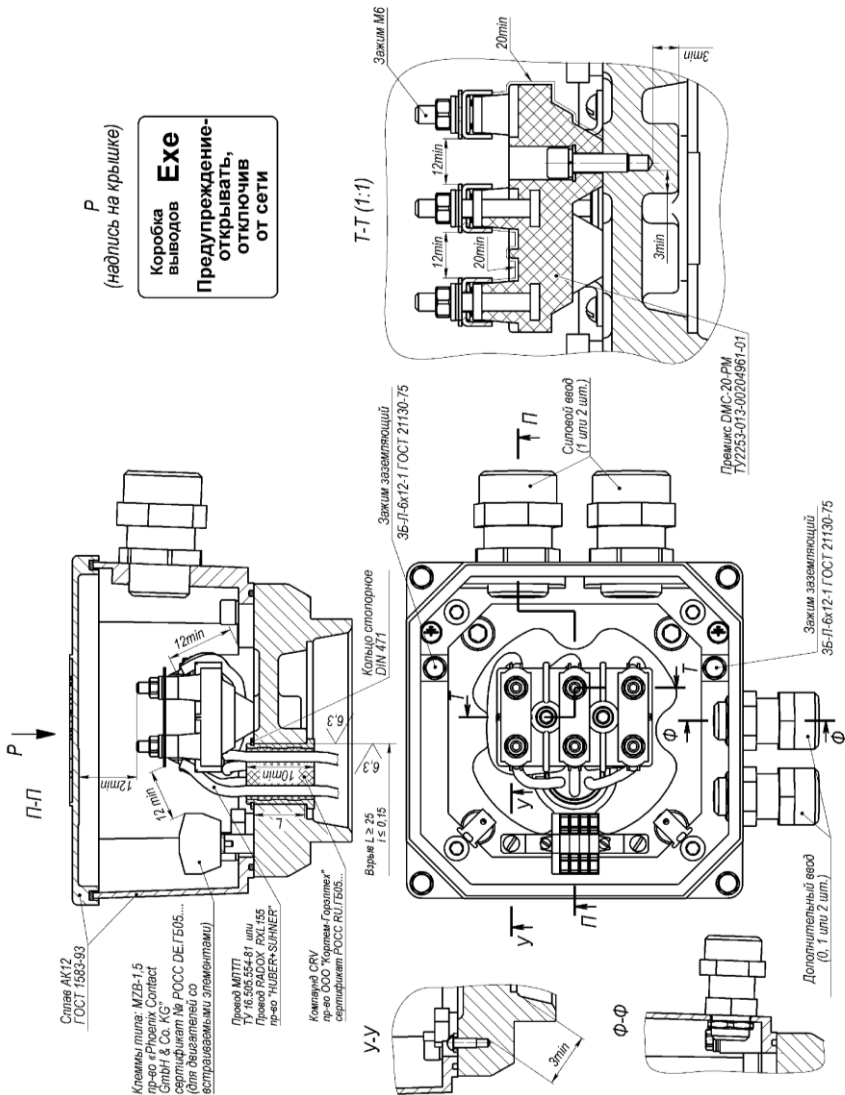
Чертеж взрывозащиты коробки выводов «Ехе»
